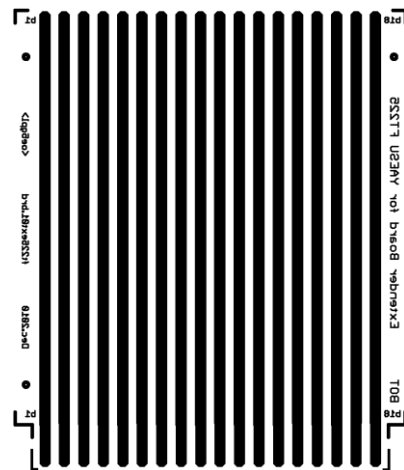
Rückseitiges Layout direkt gesteckter FT225-Adapter (nicht maßstabgetreu)
